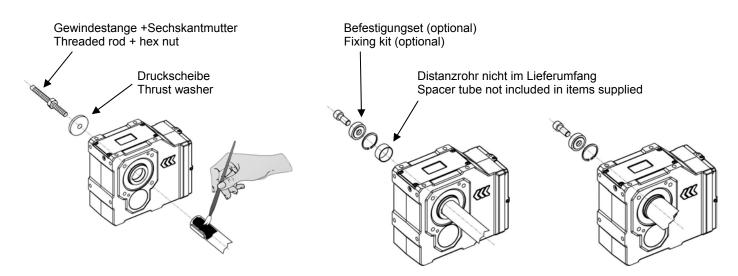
Aufziehen der Kundenwelle ohne oder mit Anlageschulter
